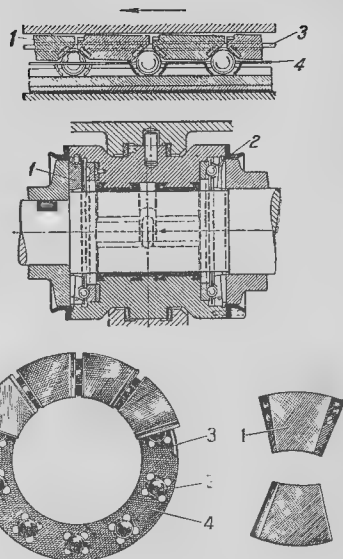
Разрез и детали упорного подшипника Броун Бовери.
